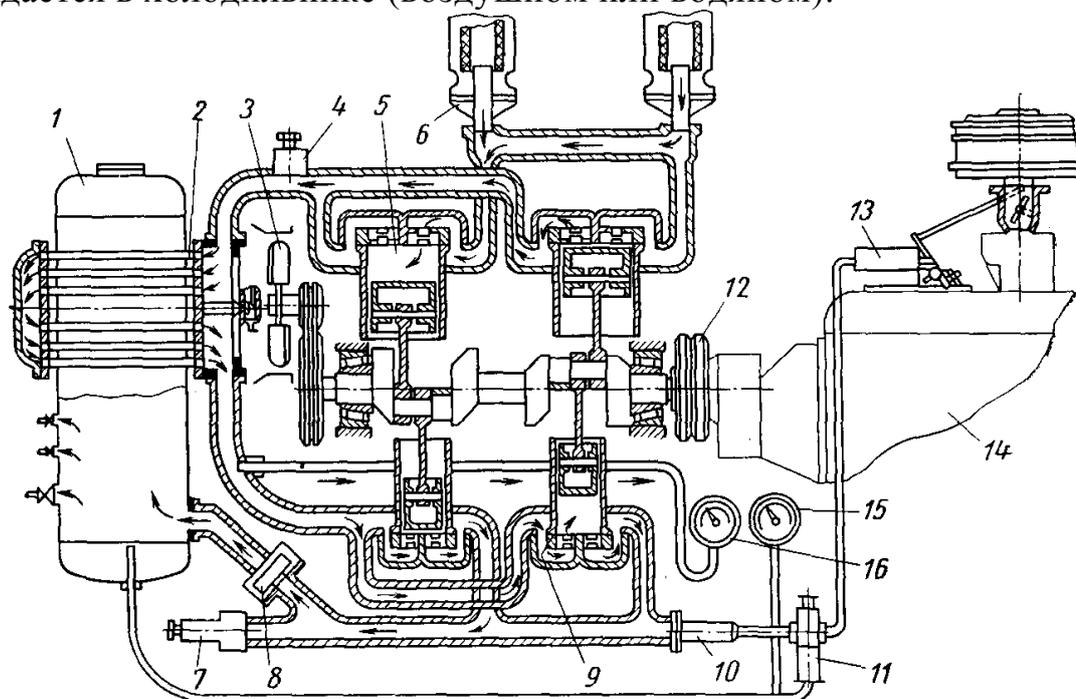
Схема двухступенчатого сжатия в V-образном компрессоре передвижной компрессорной станции:
